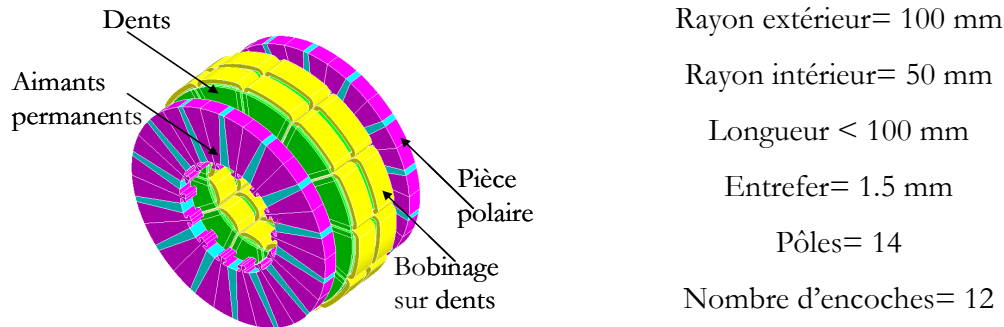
Géométrie globale de la machine et récapitulatif des dimensions
